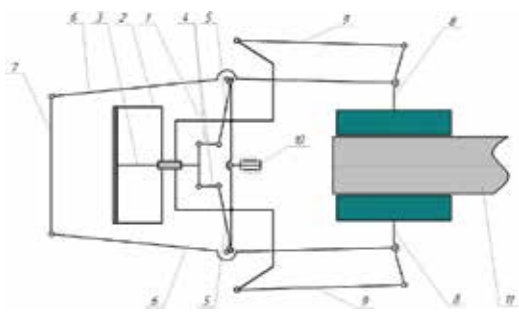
Структурная схема механизма тормозного блока 743. 1 — корпус; 2 — цилиндр пневмопривода; 3 — поршень пневмопривода; 4 — жесткие звенья; 5 — поводки; 6 — рычаги-клещи; 7 — регулятор зазора между накладками и диском; 8 — колодки с закрепленными на них фрикционными накладками; 9 — жесткие звенья, образующие параллелограммные контуры; 10 — подвес к раме тележки; 11 — тормозной диск
